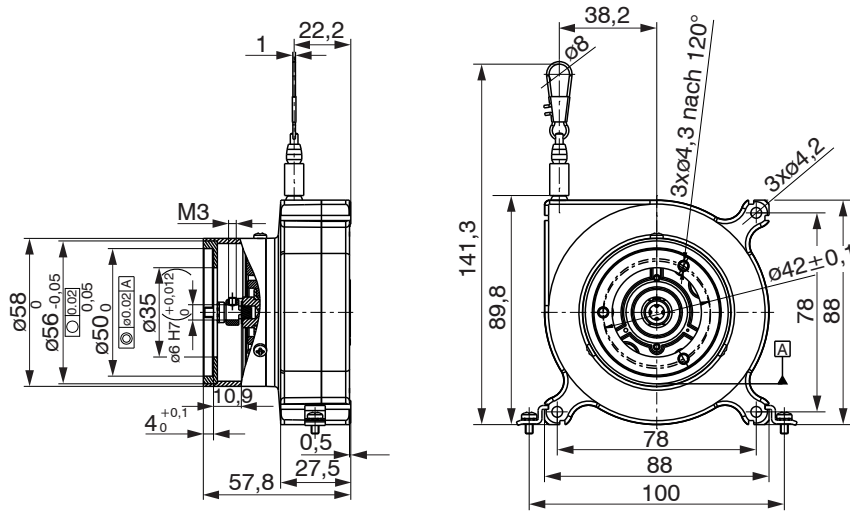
Maßzeichnung WPS-xxx-MK88-M, Abmessungen in mm
